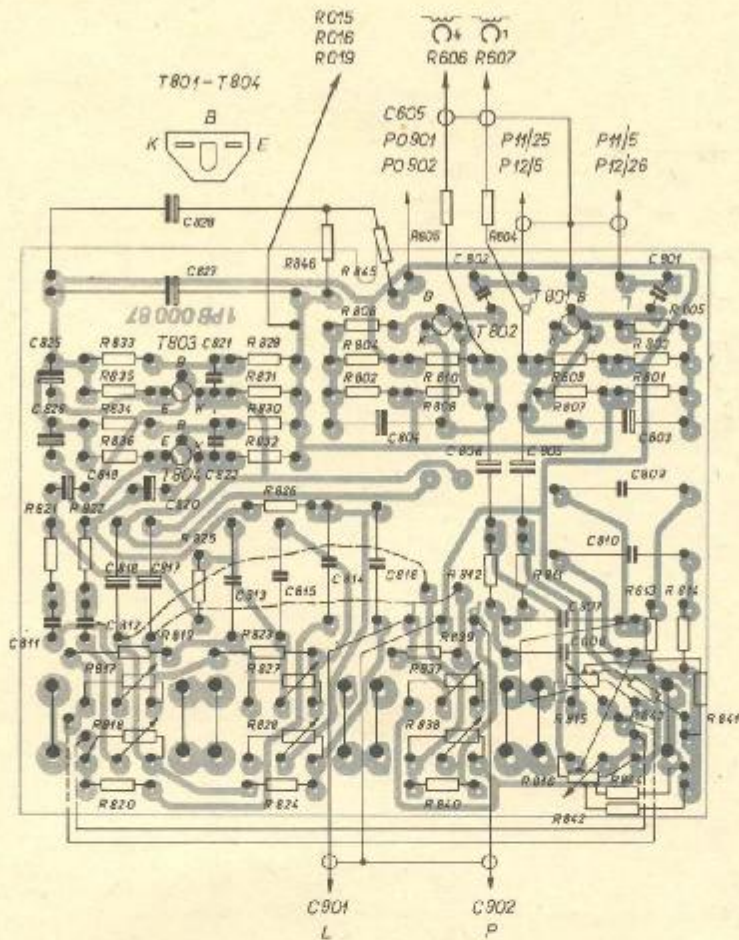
Montážní zapojení korekčního předzesilovače pro přenosku
